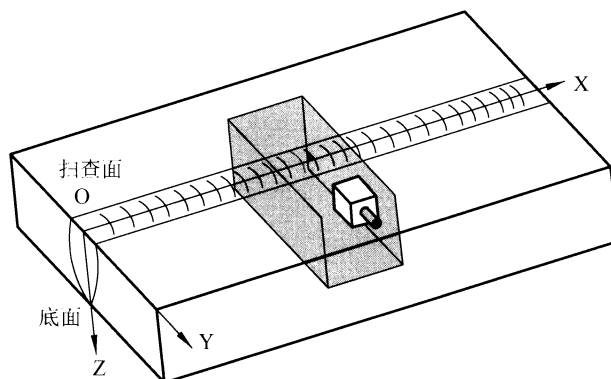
焊接接头检测全聚焦 3D 型显示
